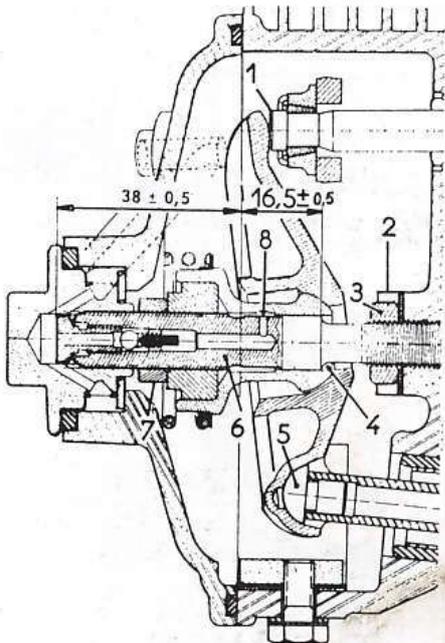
Vue en coupe d'une chambre de culbuteur.
